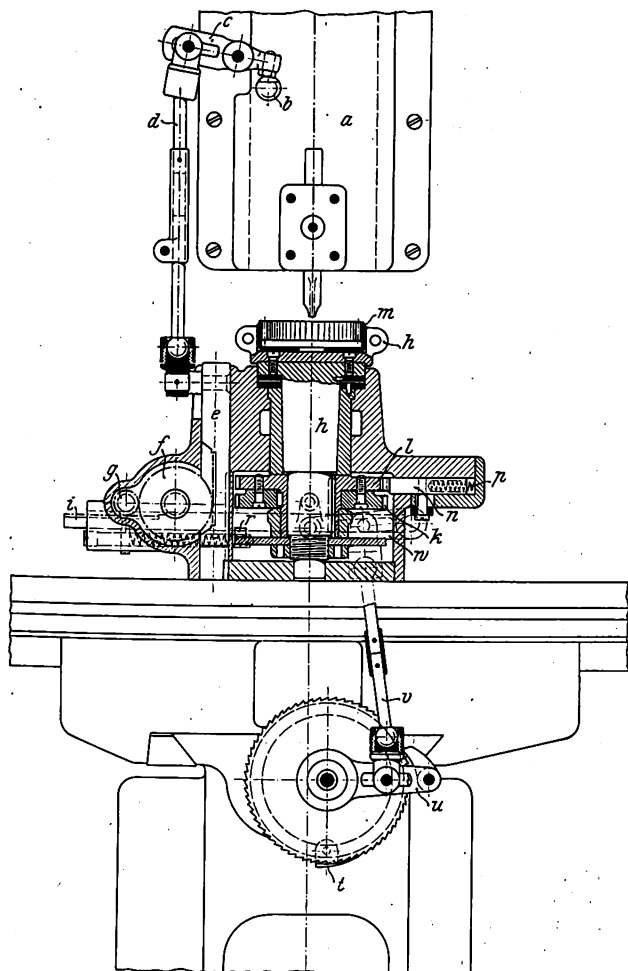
und 3. Fräsmaschine der Wanderer-Werke vorm. Winkelhofer & Jänicke mit Stoßvorrichtung.
